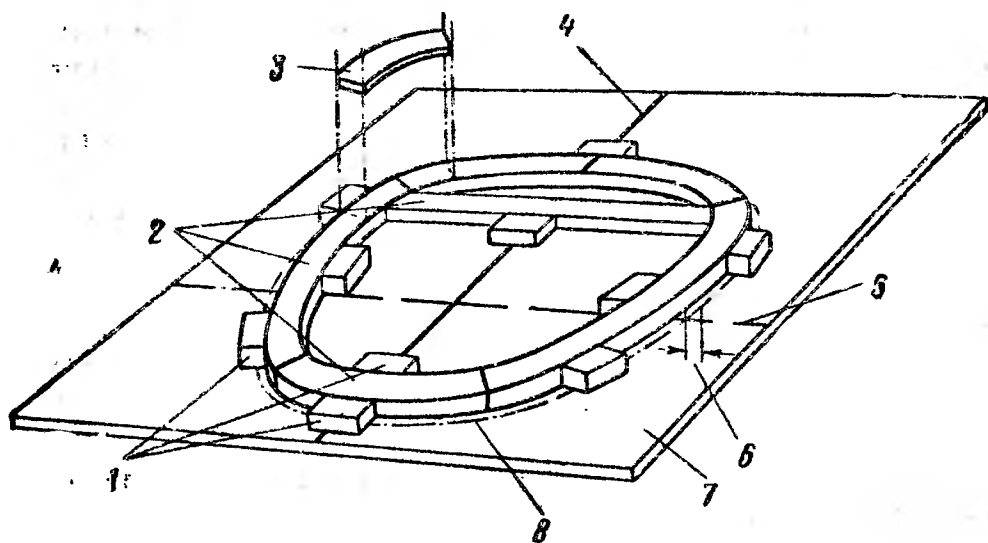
Плаз для сборки шпангоута: 1 — бобышки, ограничивающие установку реек шпангоута; 2 — рейки шпангоута; 3 — фанерная кница, скрепляющая рейки; 4 — вертикальная ось шпангоута; 5 — горизонтальная ось шпангоута; 6 — размер толщины обшивки корпуса; 7 — лист фанеры; 8 — контур обвода шпангоута по размерам теоретического чертежа (с обшивкой).
